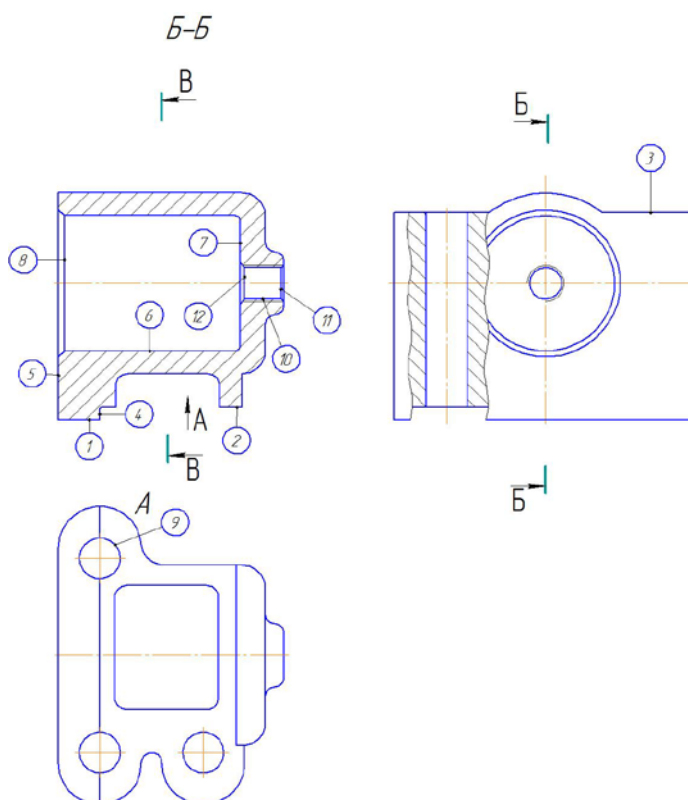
Эскиз детали с номерами обрабатываемых поверхностей
